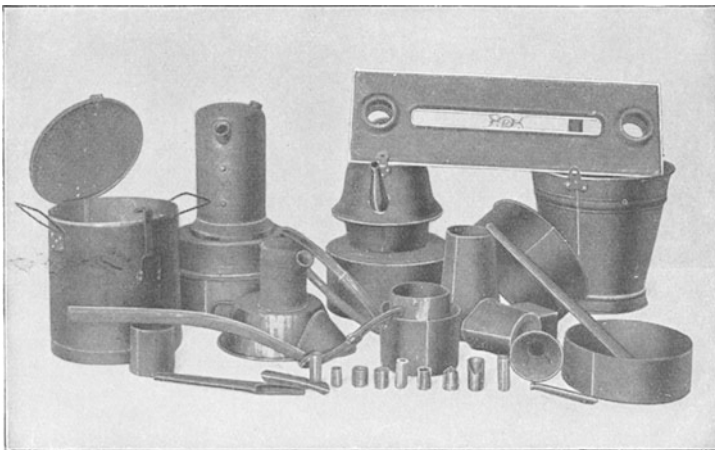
Beispiele von Nahtschweißungen.
